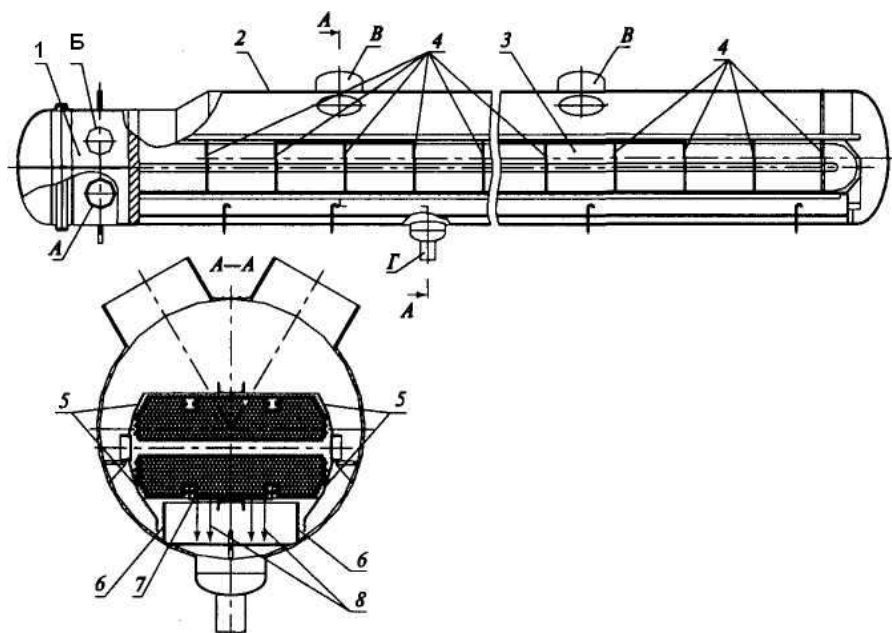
Горизонтальный подогреватель низкого давления ПНД-1.
